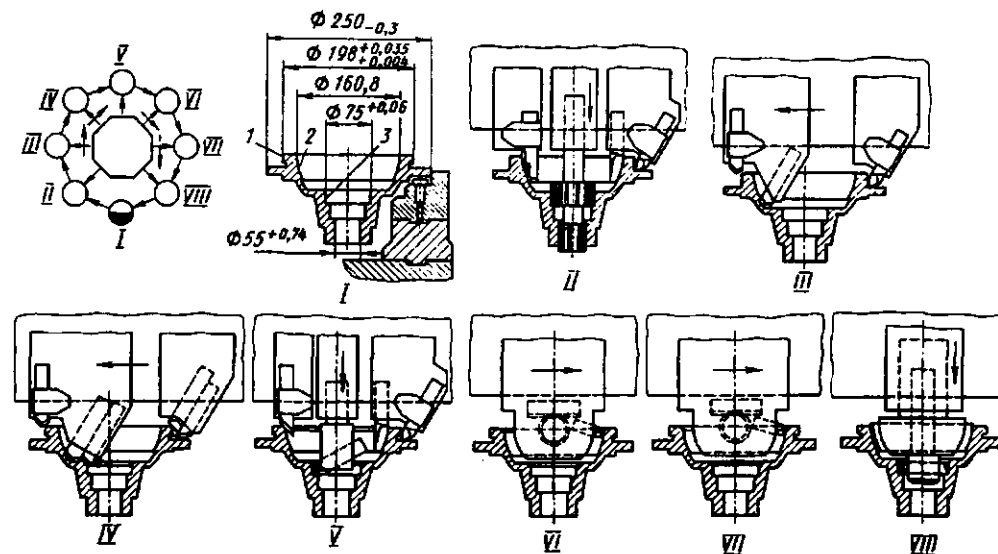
Наладка восьмишпиндельного полуавтомата для обработки фасонной заготовки
